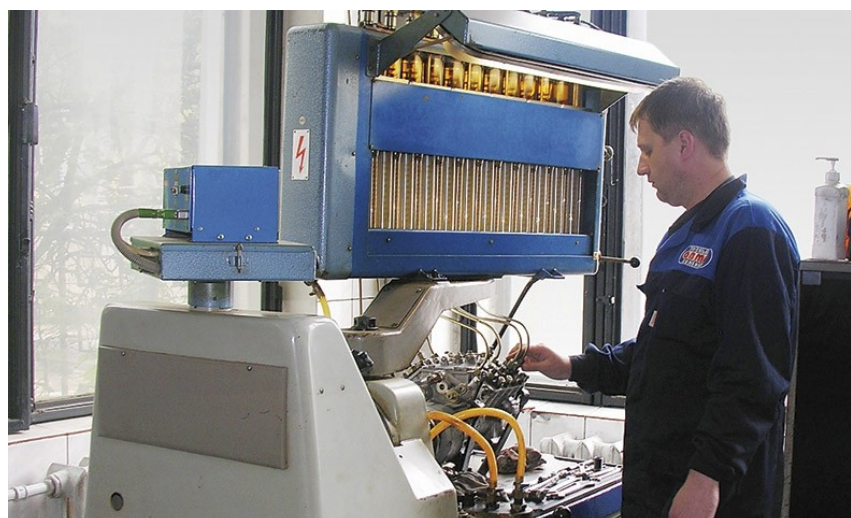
Станок для проверки топливных насосов высокого давления
